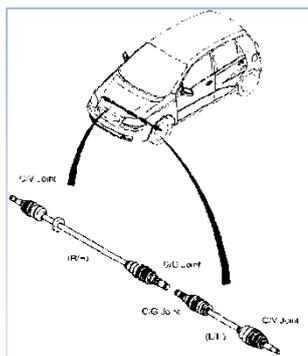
Montaje de Puntas de Eje en la Transmisión
